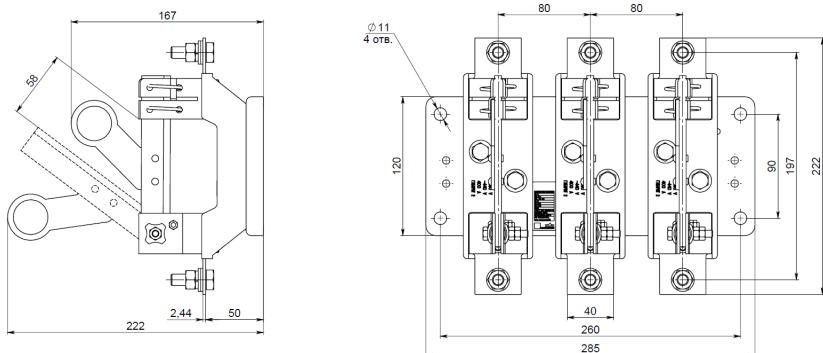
Разъединитель РЕ19-37-31190-00 УХЛЗ с центральным рычагом для управления штангой, масса 3,82 кг
